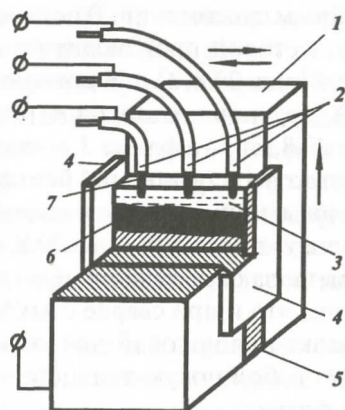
Схема электрошлаковой сварки:
